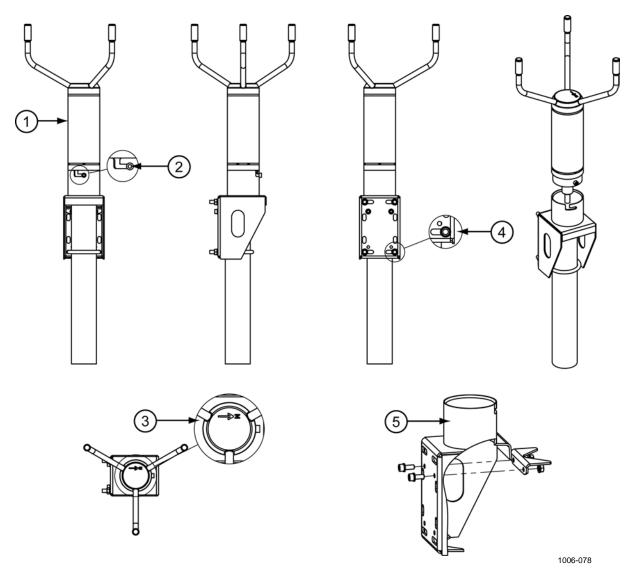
Установка датчика ветра WMT700 на вершине мачты
